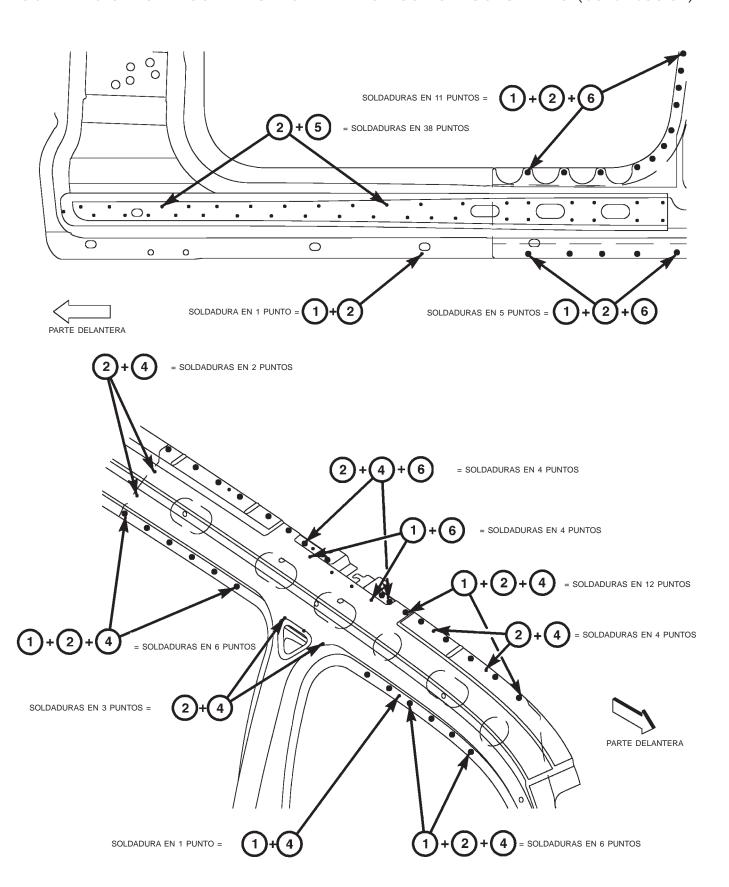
PLANCHAS LATERALES DE LA CARROCERIA INFERIOR Y SUPERIOR
